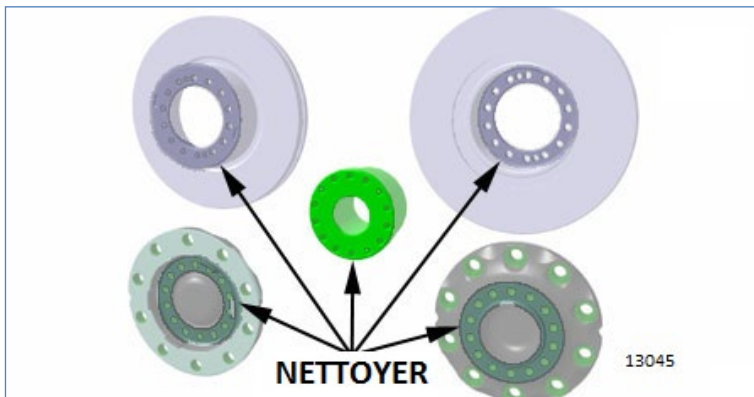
NETTOYAGE DES SURFACES DE CONTACT DU ROULEMENT DE MOYEU, DU DISQUE ET DE LA BRIDE DE MOYEU
